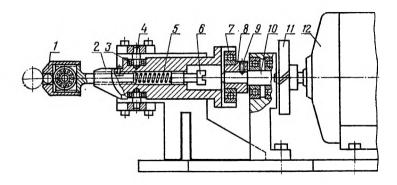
Виброголовка к токарному станку для обработки наружных цилиндрических поверхностей:
